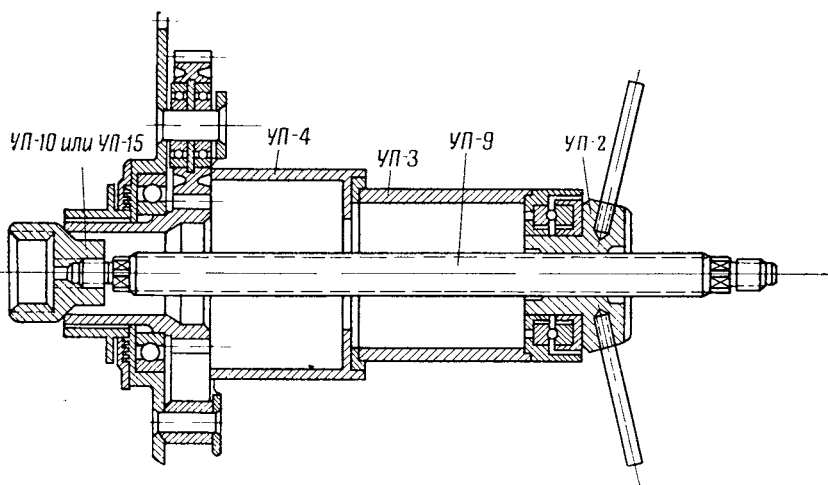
Универсальное приспособление 48001-1-074УП, снятие солнечной шестерни планетарного механизма
